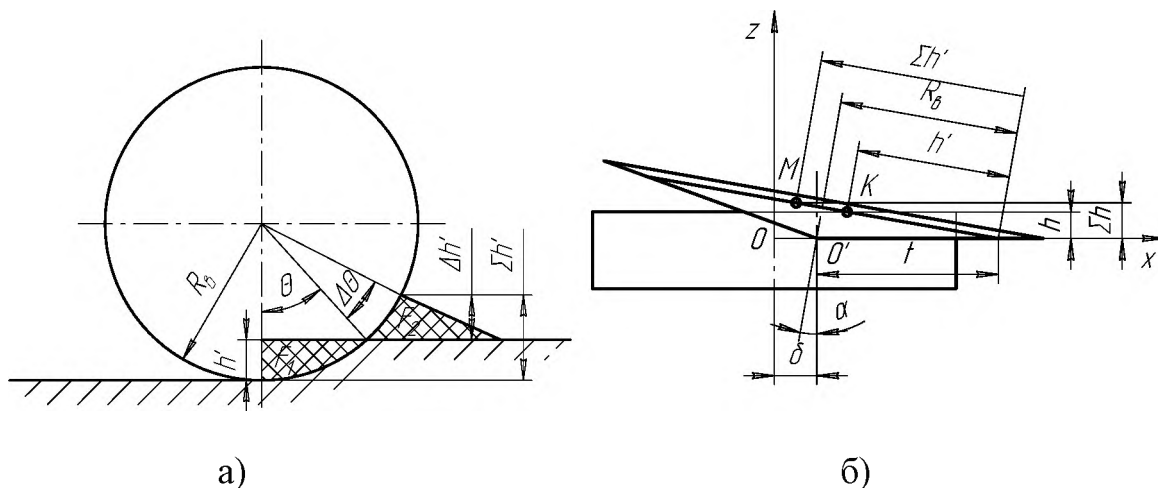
До визначення площі контакту валка із заготовкою із врахуванням пластичної хвилі
